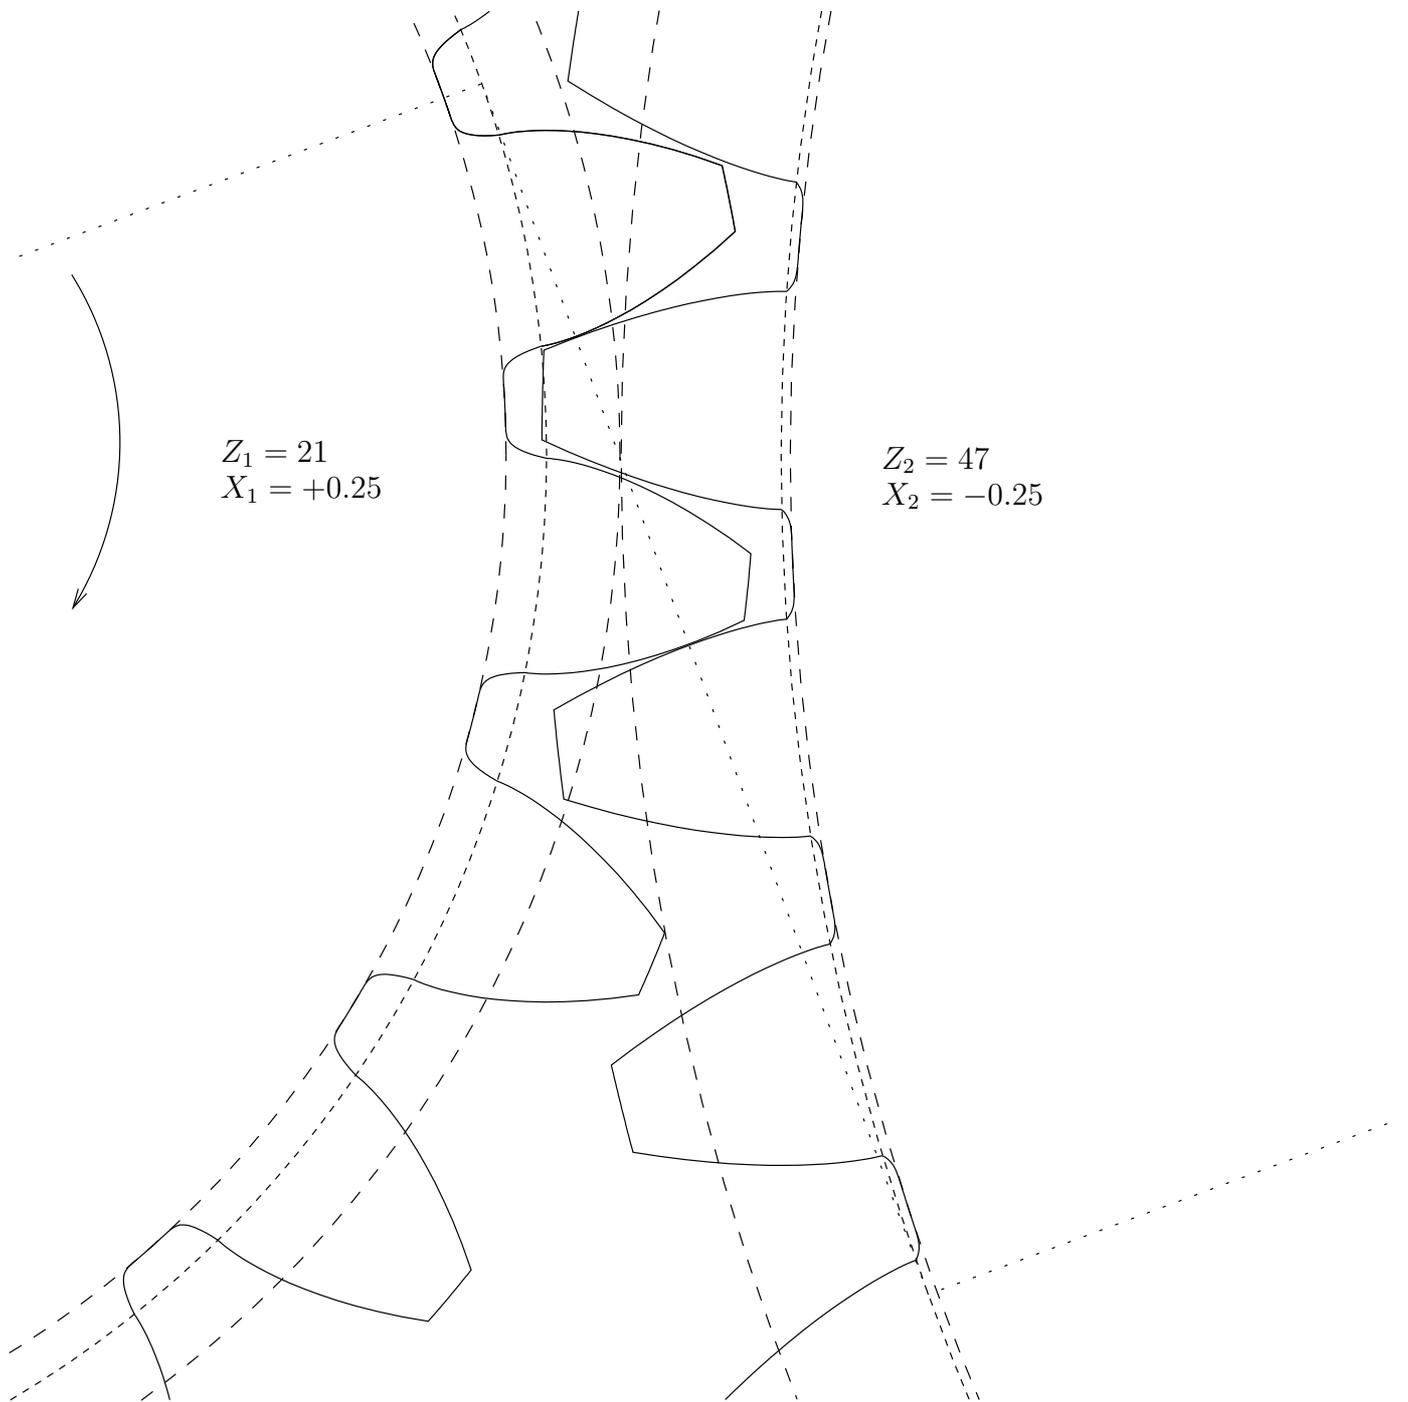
Représentation du contact au niveau d'un engrenage (module 4 mm)
